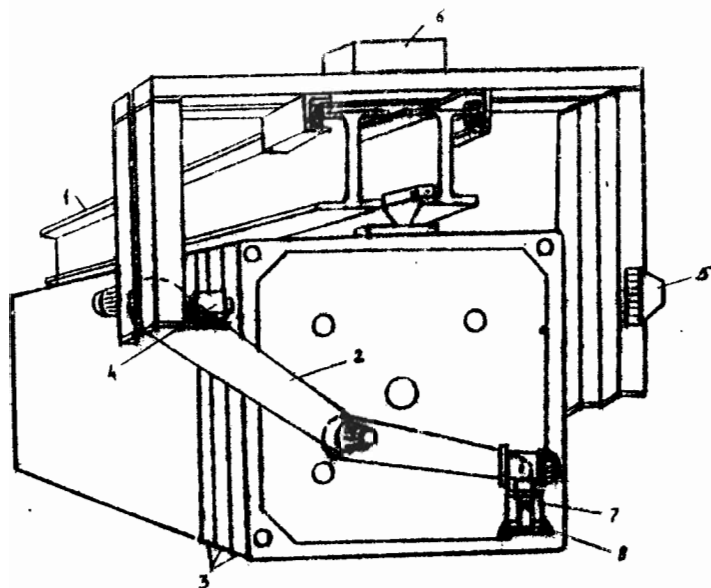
Фильтр-пресс [43]. 1 — горизонтальная несущая балка с транспортной тележкой; 2 — манипулятор; 3 — плиты фильтр-пресса; 4 — видеокамера; 5 — фара; 6 — привод; 7 — захват; 8 — сменные устройства для удаления осадка с рам.
